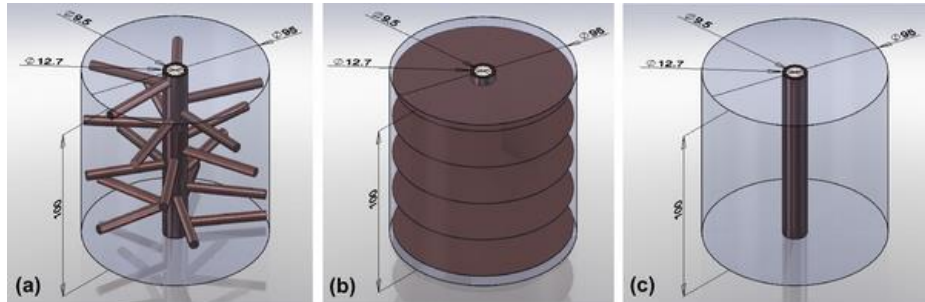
Géométries testées par Tay et al. [198]. (a) Tube clouté ; (b) Tube à ailettes radiales ; (c) Tube lisse.
